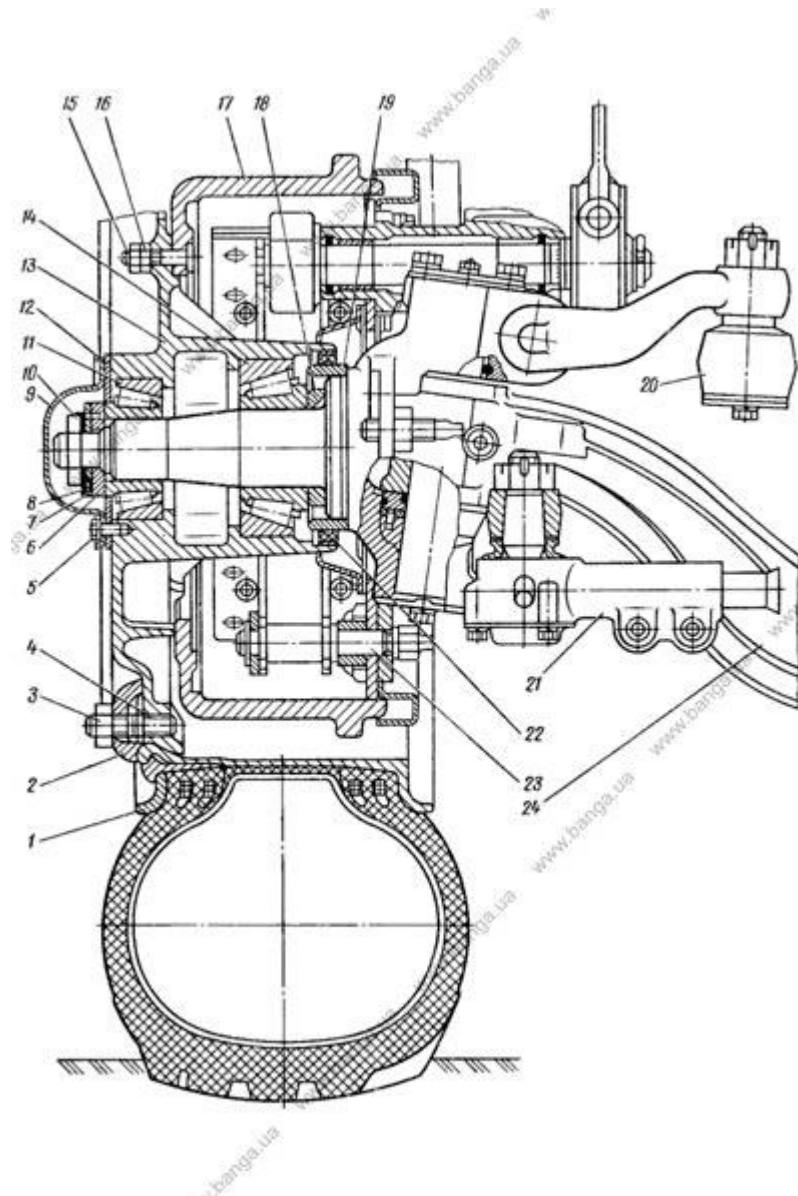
Передня вісь у зборі зі маточинами, колесами, гальмівним механізмом і тягою рульової трапеції: 1- колесо з шиною в зборі; 2-притиск колеса; 3. 16-гайки; 4 шпильки; 5-болт з шайбою в зборі; 6-гайка підшипників; 7-замкова шайба гайки; 8-замкова шайба контргайки; 9-кришка маточини; 10-контргайка; 11, 14-підшипники; 12-прокладки; 13-ступиця; 15-болт; 17-гальмівний
